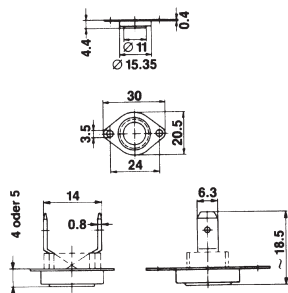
Flansch mit beidseitiger Befestigung abgesetzt
